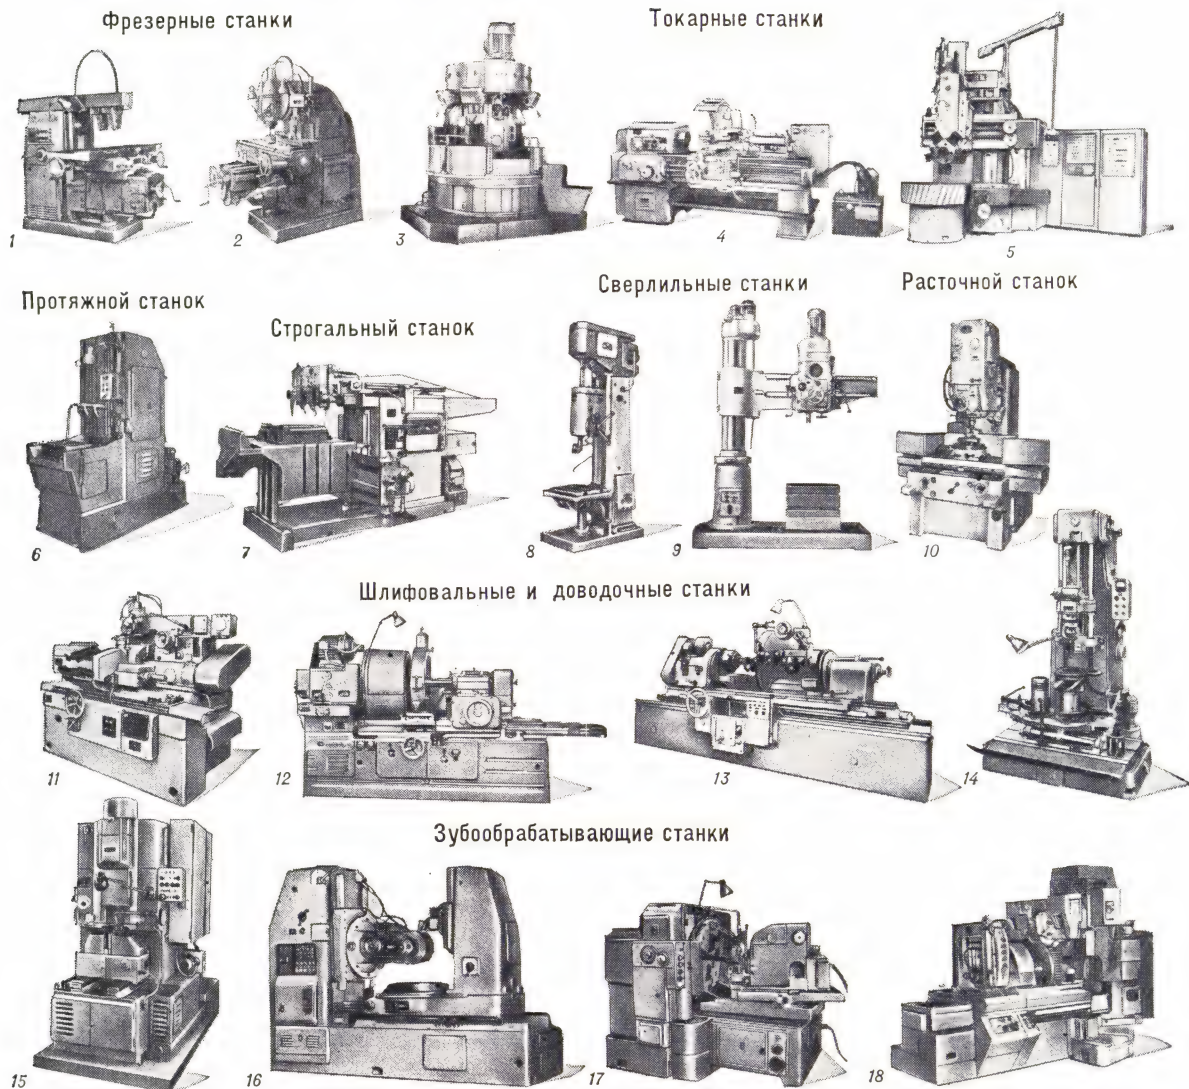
Основные типы металлорежущих станков: 1 — универсальный консольно-фрезерный станок (6Н12К); 2 — вертикально-фрезерный станок с копировальным устройством (6Н12К); 3 — токарный восьмишпиндельный автомат (1К282); 4 — универсальный токарно-винторезный станок с автоматическим циклом (1К62А); 5 — токарно-карусельный одностоечный станок с числовым программным управлением (1512Ф2); 6 — вертикально-протяжной станок (7Б705); 7 — копировальный поперечно-строгальный станок (ГД-21); 8 — вертикально-сверлильный станок (2А135); 9 — радиально-сверлильный станок (2А53); 10 — координатно-расточный станок (2Б440); 11 — круглошлифовальный автомат (3К161); 12 — внутришлифовальный станок (3З60); 13 — станок для перешлифовки шатунных и коренных шеек коленчатых валов (3А423); 14 — хонинговальный вертикальный одношпиндельный станок (3Б833); 15 — зубодолбежный полуавтомат (5122); 16 — зубофрезерный станок (5К328А); 17 — зубострогальный полуавтомат (5А250П); 18 — зубошлифовальный станок (5Б53).
